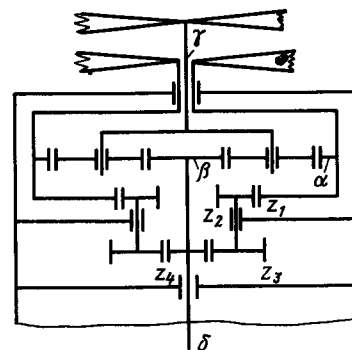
Кинематическая схема низкооборотной ступени редуктора вертолетного ГТД
